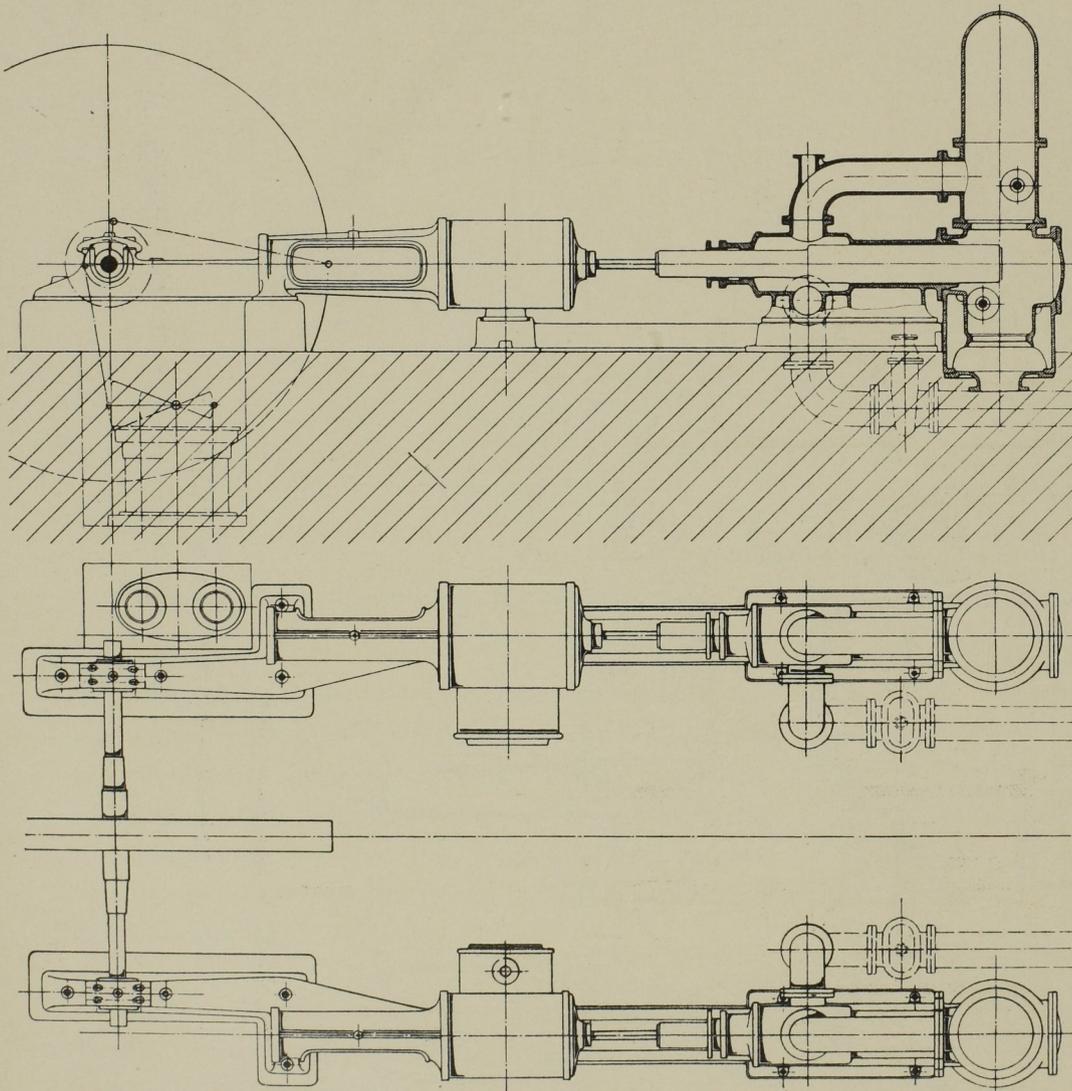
Seitenansicht und Grundriss der Pumpmaschine für Wyhlen. Masst. 1:50.
